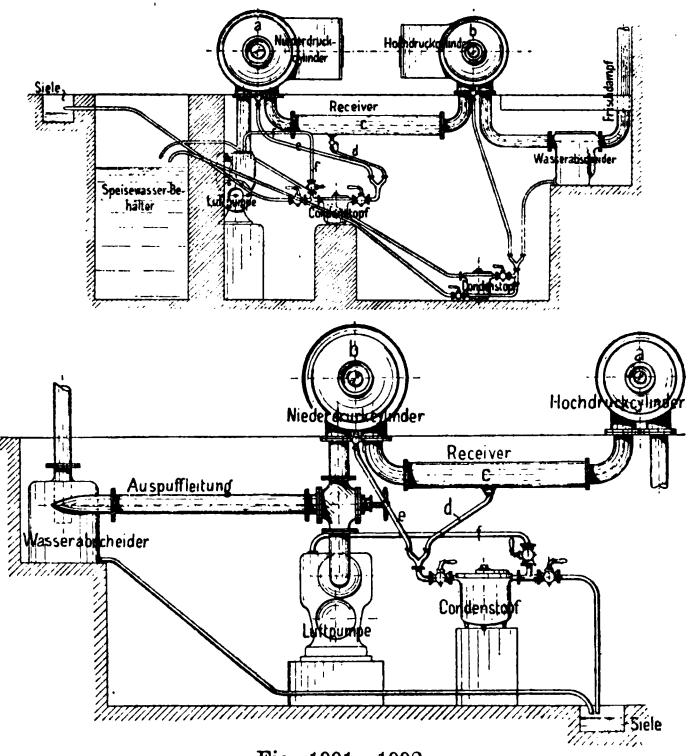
1992. Entwässerung der Kompoundmaschine.
